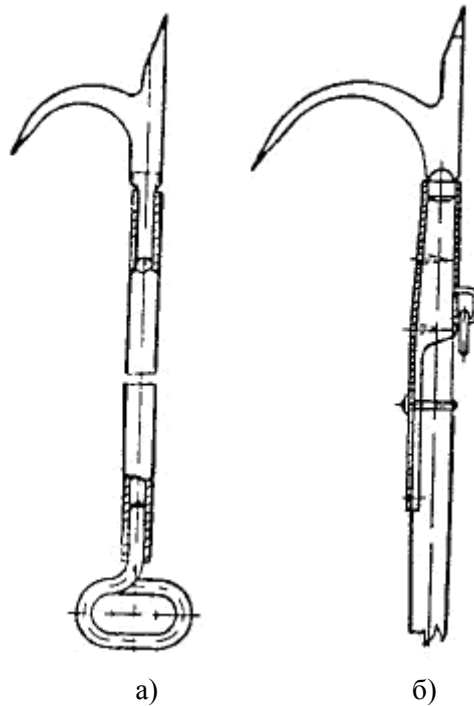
Пожежні багри: а) багор пожежний металевий; б) багор пожежний насадний
